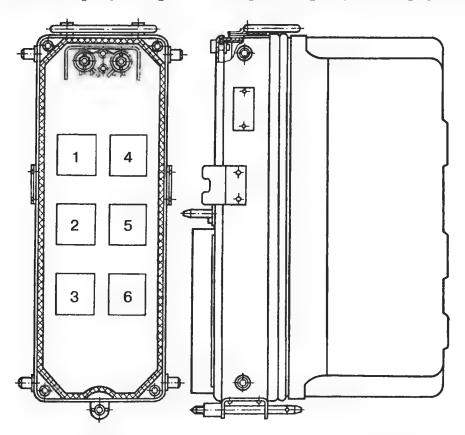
Релейный блок маршрутного набора и расположение приборов
